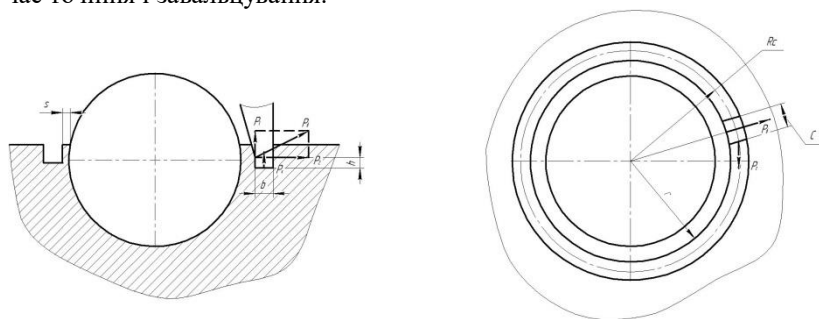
Розрахункова схема для розрахунку інструмента для завальцювання кульки
